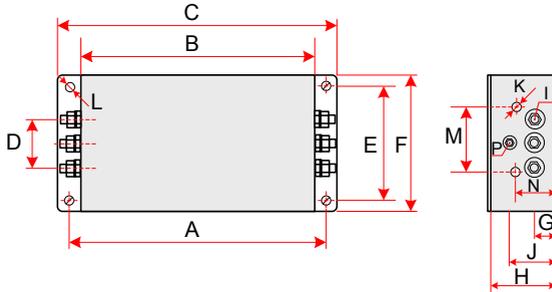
强力滤波器 50-180A 尺寸图 (单位: mm)
